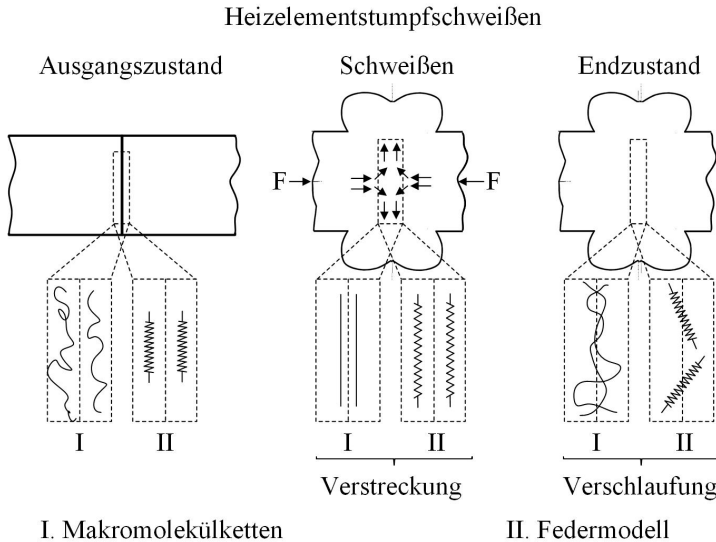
Anordnung der Makromolekülketten bei einer Heizelementstumpfschweißung und Beschreibung als Federmodell im Ausgangszustand (links), während des Schweißens (mittig) und im Endzustand (rechts)
